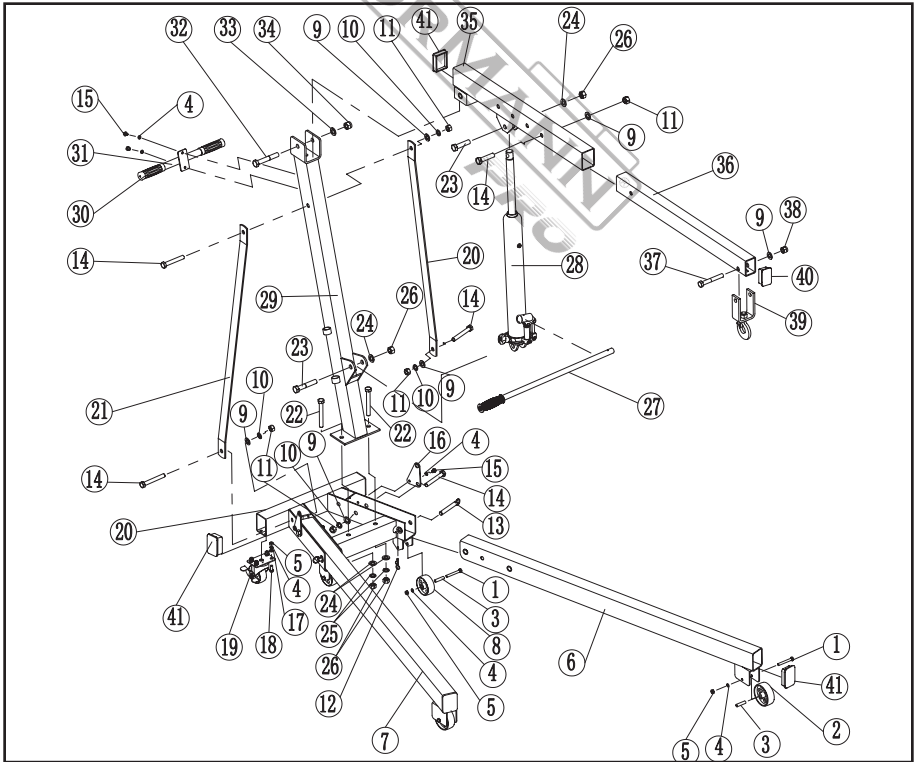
Schema di assemblaggio della gru con motore idraulico
